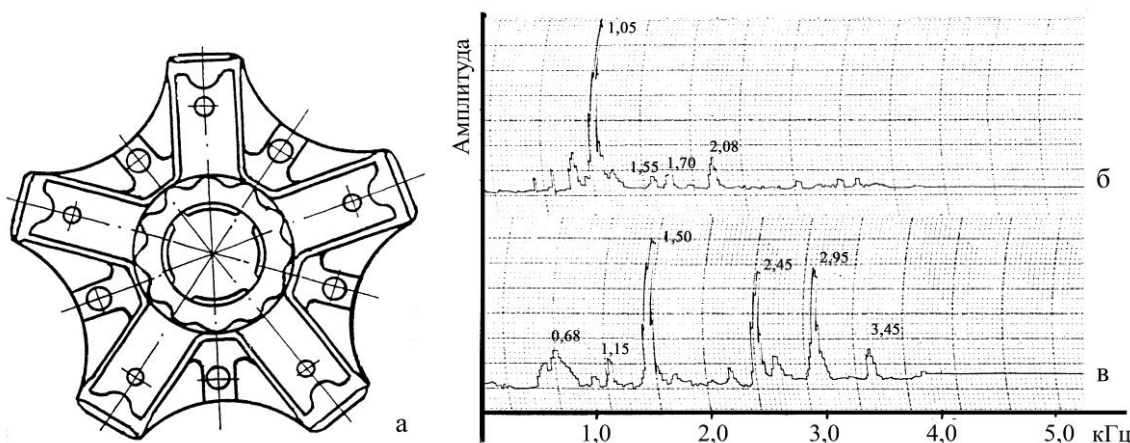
Акустический контроль ступицы заднего колеса автомобиля «КАМАЗ». а – отливка, б – спектр для отливки из серого чугуна, в – спектр для отливки из высокопрочного чугуна
